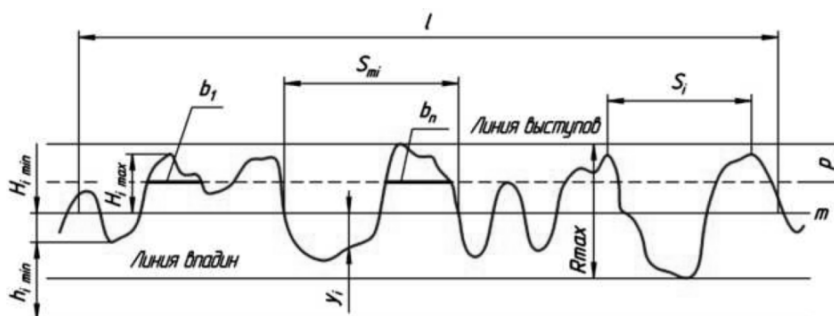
Нормальный профиль и параметры шероховатости поверхности
